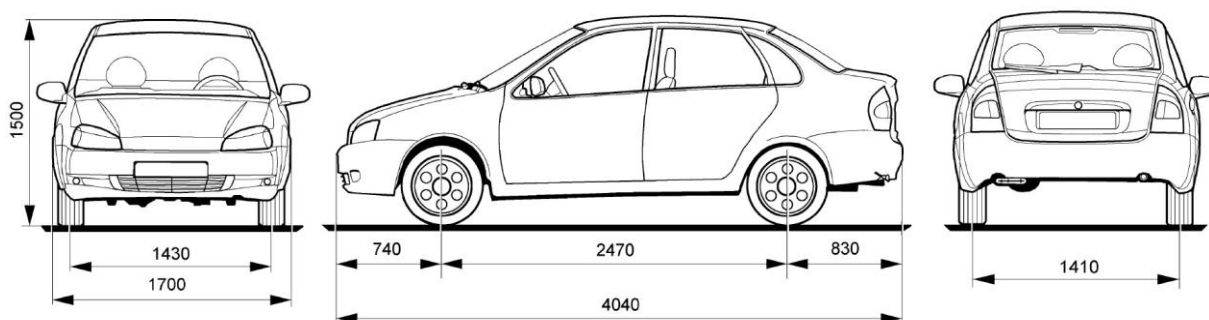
Габаритные размеры автомобиля LADA Kalina
